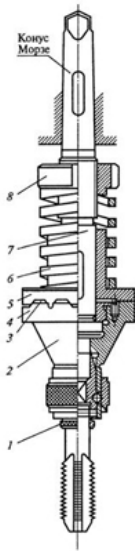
Предохранительный патрон для нарезания резьбы в глухих и сквозных отверстиях:
